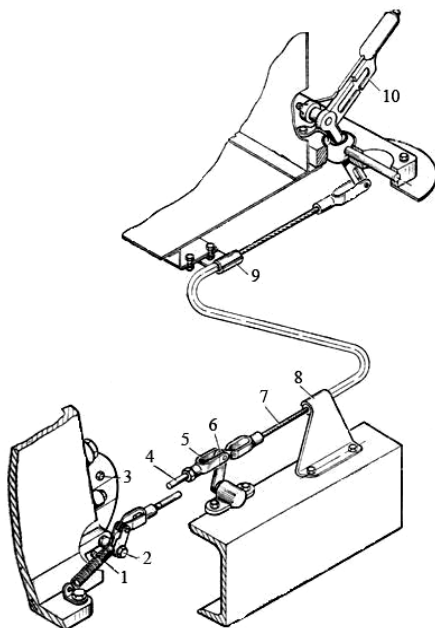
Схема приводу керування клапанним механізмом редуктора ВВП тракторів Т-150 і Т-150К:
